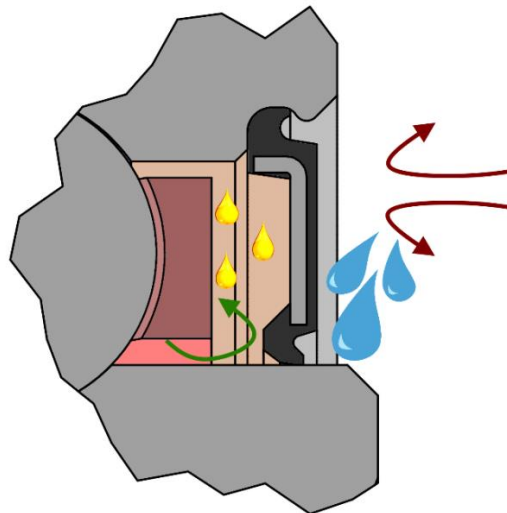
Prinzip einer Dichtstelle; © Artur Küpper GmbH & Co KG 2016
